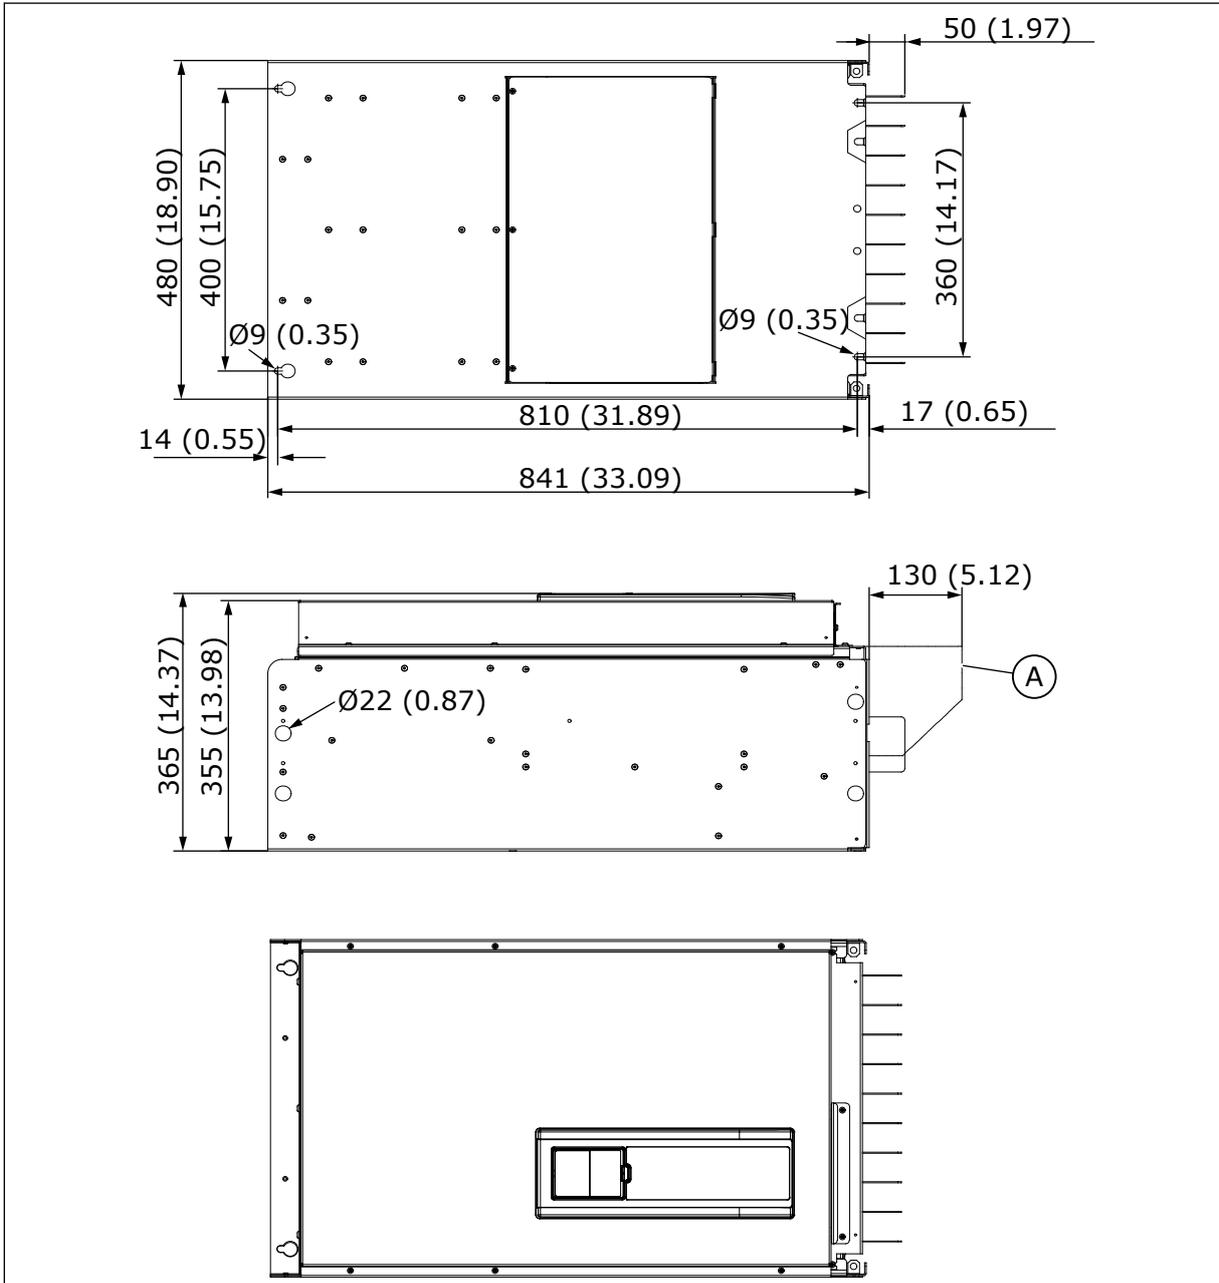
Габариты преобразователя частоты, корпуса MR9 и MR11 [мм (дюймы)]
